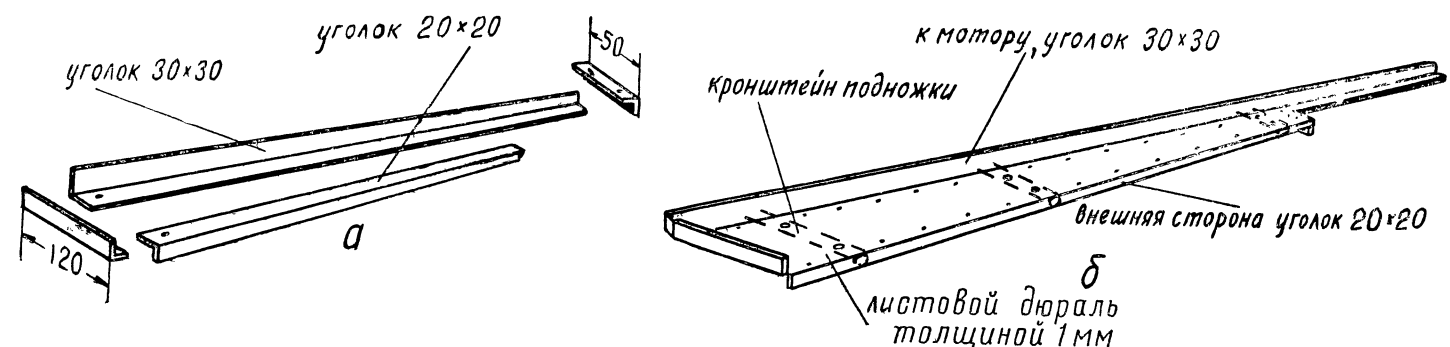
Левая подножка мотороллера: а — заготовка уголков для подножки; б — подножка в сборе
